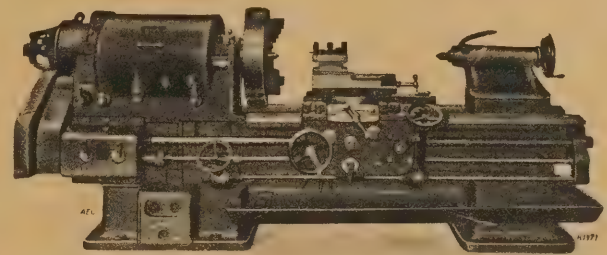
Schnelldrehbank mit Drehstrom-Flanschmotor, eingebauter Wende-Steuerwalze und Einbau-Schalttafel.
